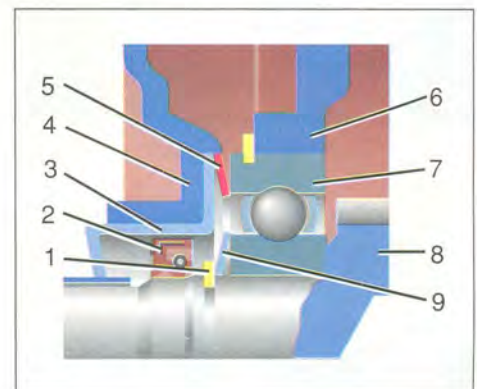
Задний подшипник ведущего вала: 1 – стопорное кольцо; 2 – сальник; 3 – передняя крышка; 4 – картер сцепления; 5 – пружинная тарельчатая шайба; 6 – картер коробки передач; 7 – подшипник; 8 – ведущий вал; 9 – пружинная шайба.
